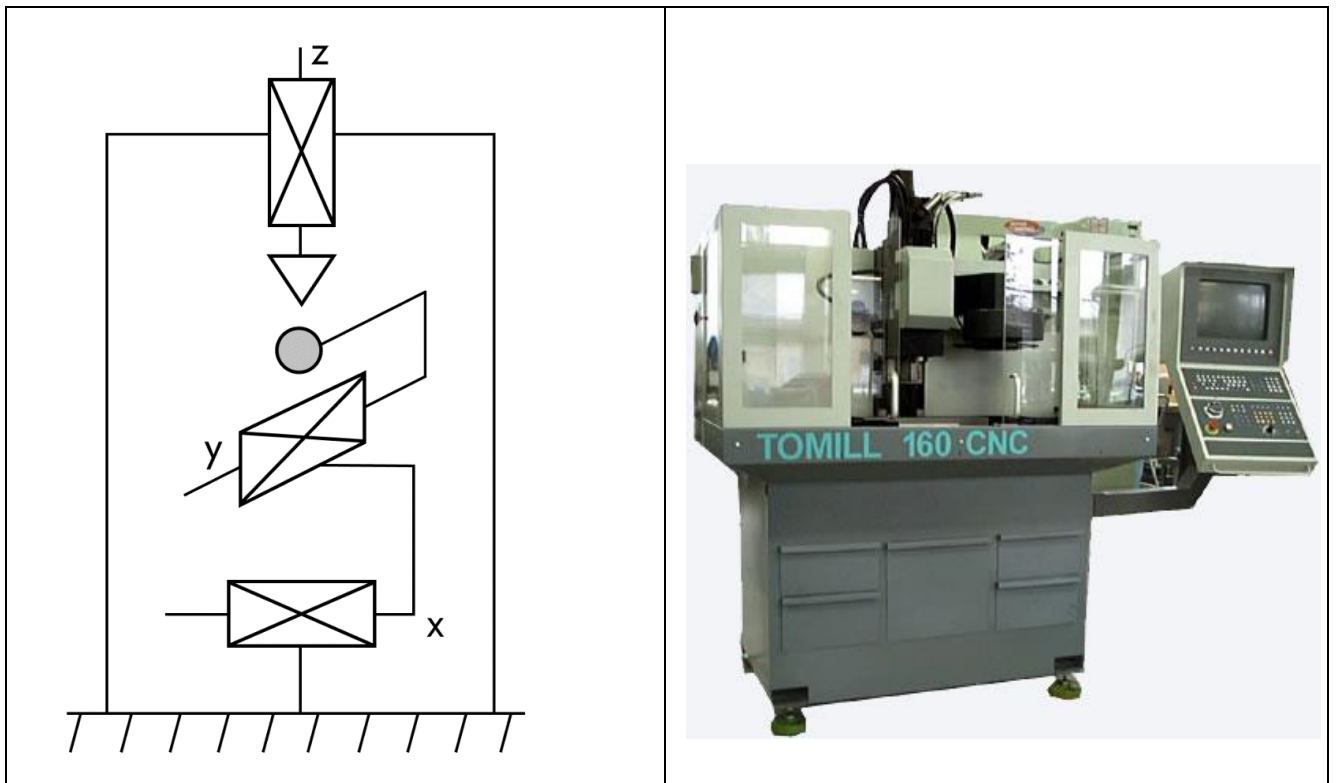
Вертикально-фрезерный обрабатывающий центр TOMILL-160 фирмы «CNT» (Венгрия): слева – схема движения, справа – внешний вид
